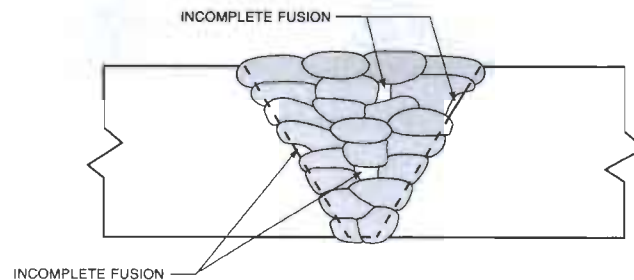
Fusión incompleta en una unión soldada
